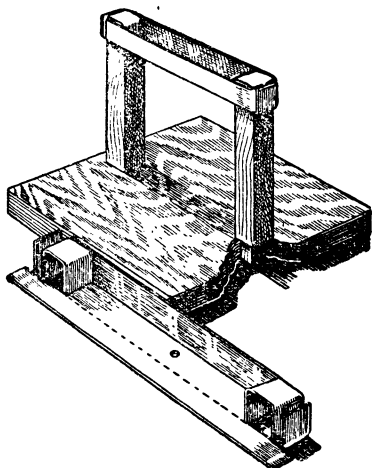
Крепление стоек в дощечке и изготовление подшипника.
